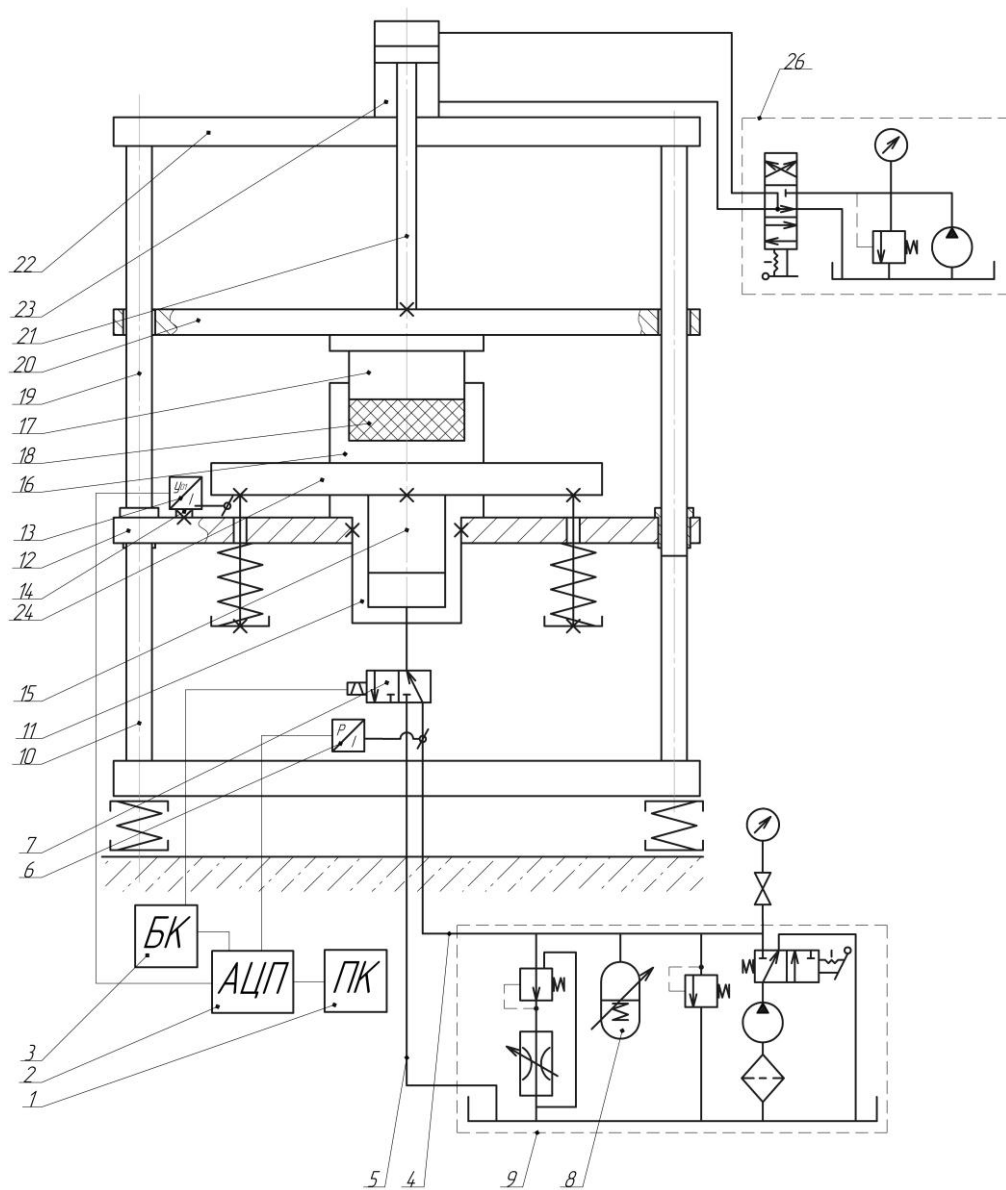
Принципова гідрокінематична схема експериментального вібропрес-молота з електрогідравлічним керування для формоутворення заготовок порошкових матеріалів
